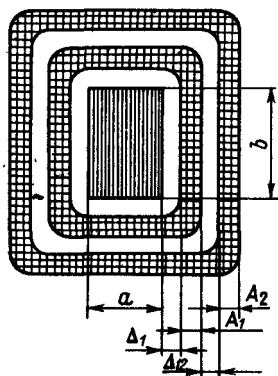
Прямоугольное поперечное сечение ИТ
